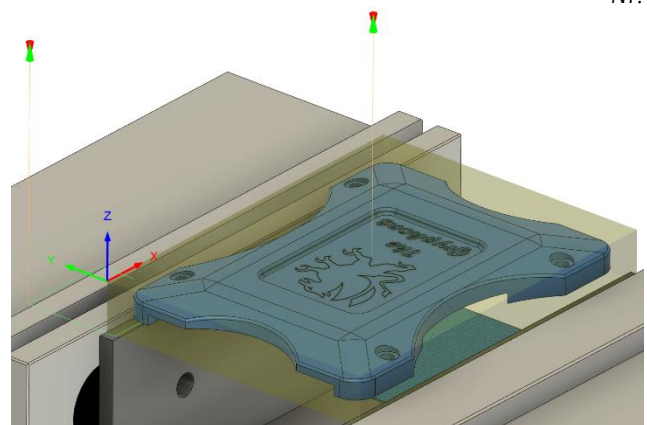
Rohteil in einem Schraubstock mit harten Backen von 6 Zoll (152 mm) befestigt
